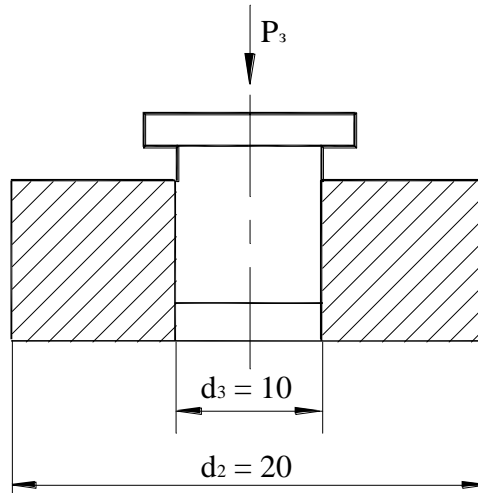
Схема з'єднання двох деталей з натягом
